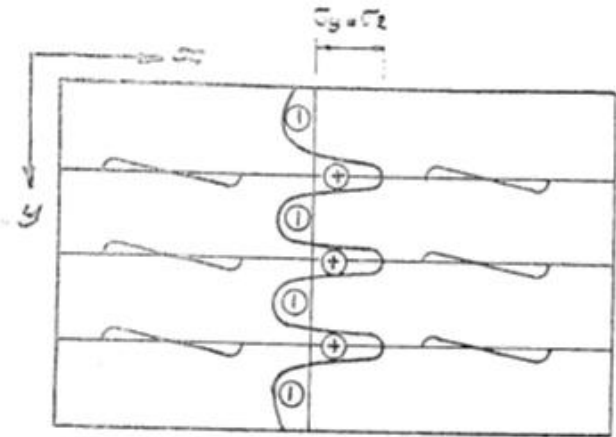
Esquema de tensões residuais em um painel soldado
